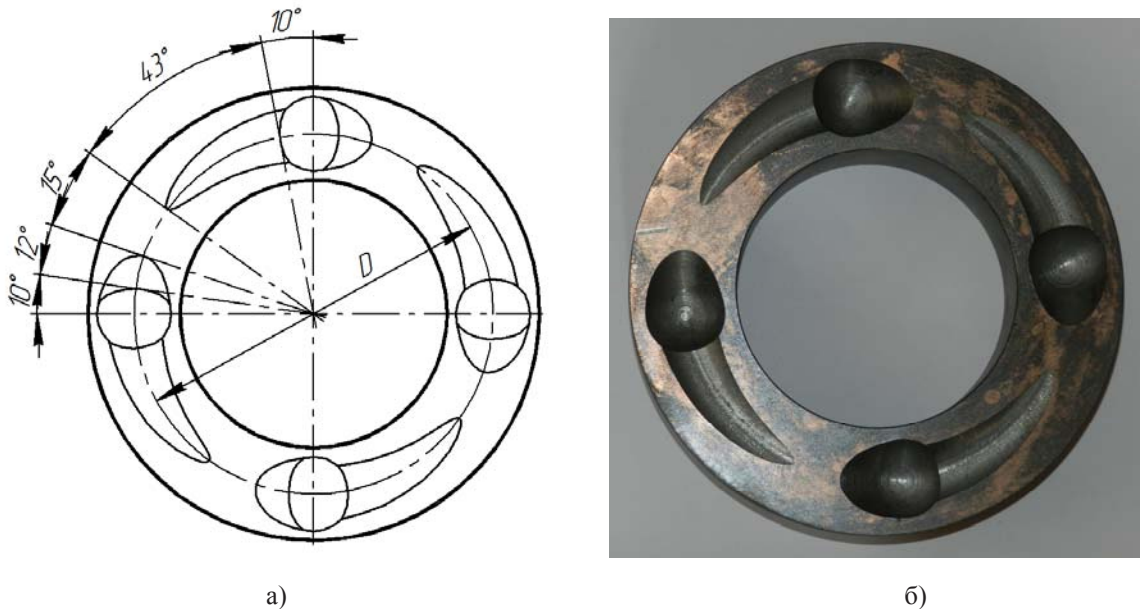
Конструктивная схема (а) и общий вид (б) рабочей поверхности ведущей полумуфты предохранительной муфты
